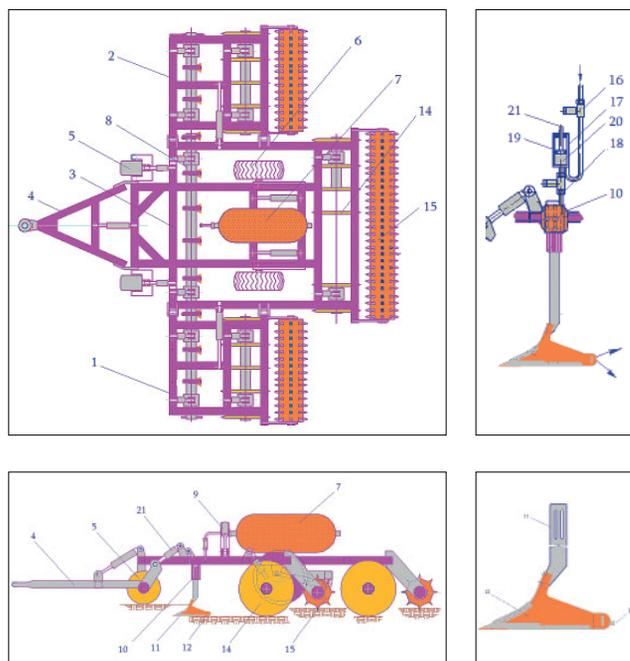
Многофункциональный комбинированный агрегат для обработки почвы импульсным воздействием ударной волны: 1, 3 – складывающиеся секции; 2 – базовая секция; 4 – сница; 5 – опорные колеса; 6 – транспортные колеса; 7 – баллон сжатого воздуха; 8 – полый вал; 9 – система пуска сжатого воздуха; 10 – полые ступицы; 11 – стойка; 12 – культиваторные лапы; 13 – пневмотрубка с выпускным клапаном; 14 – дисковые фрезы; 15 – бороны; 16, 18 – пневмоэлектродвигатели; 17 – микрорессиверы; 19 – поршень; 20 – цилиндр; 21 – винтовой механизм
